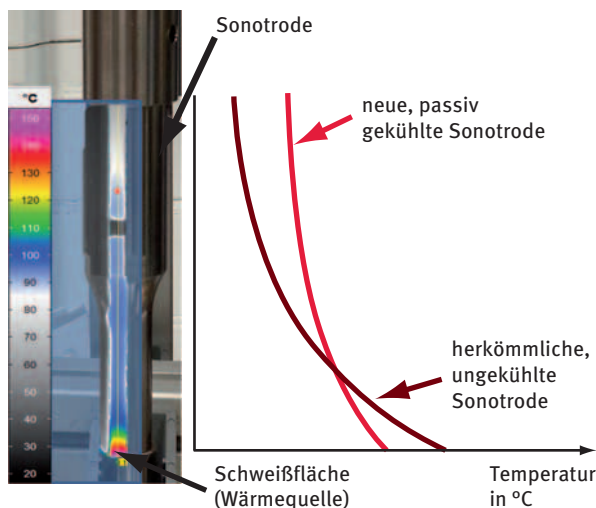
thermographische Aufnahme eines Ultraschallschweißwerkzeugs unter thermischer Belastung
